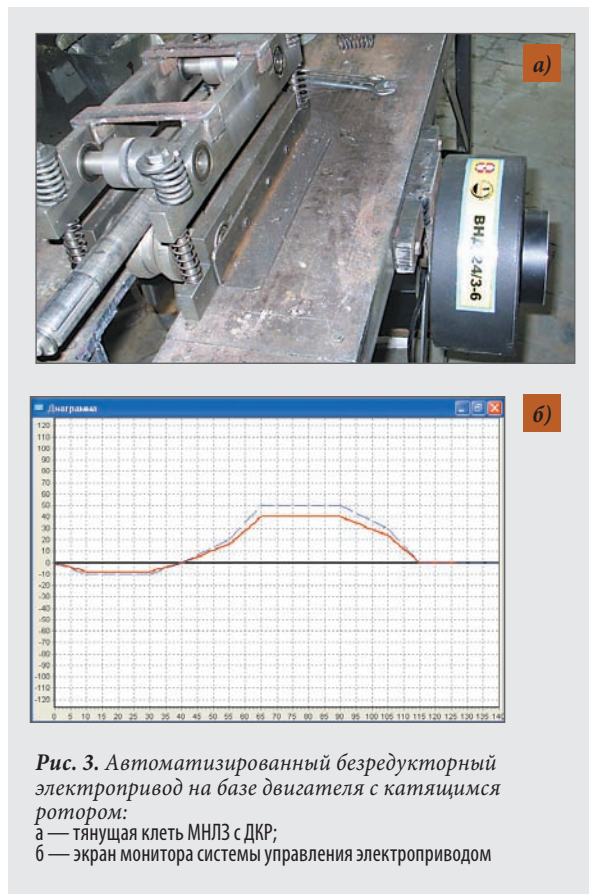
Автоматизированный безредукторный электропривод на базе двигателя с катящимся ротором:
